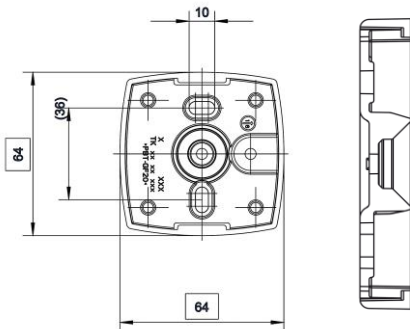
Vue en plan et en coupe de la plaque d'adaptation
